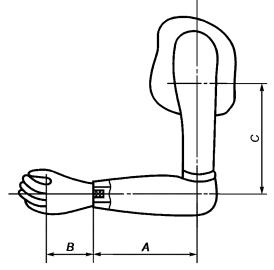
Обозначения длины сегментов образца для испытаний
